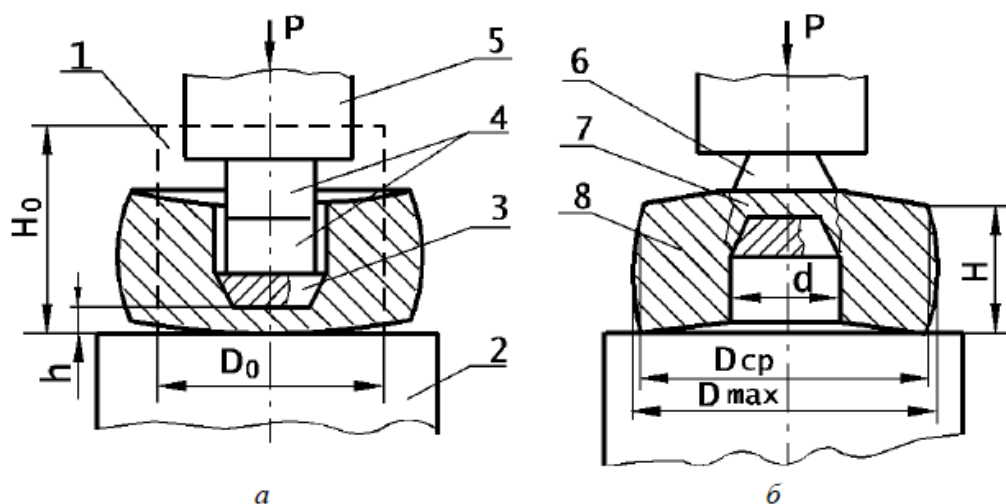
Схема открытой (а) и закрытой (б) прошивки заготовки
